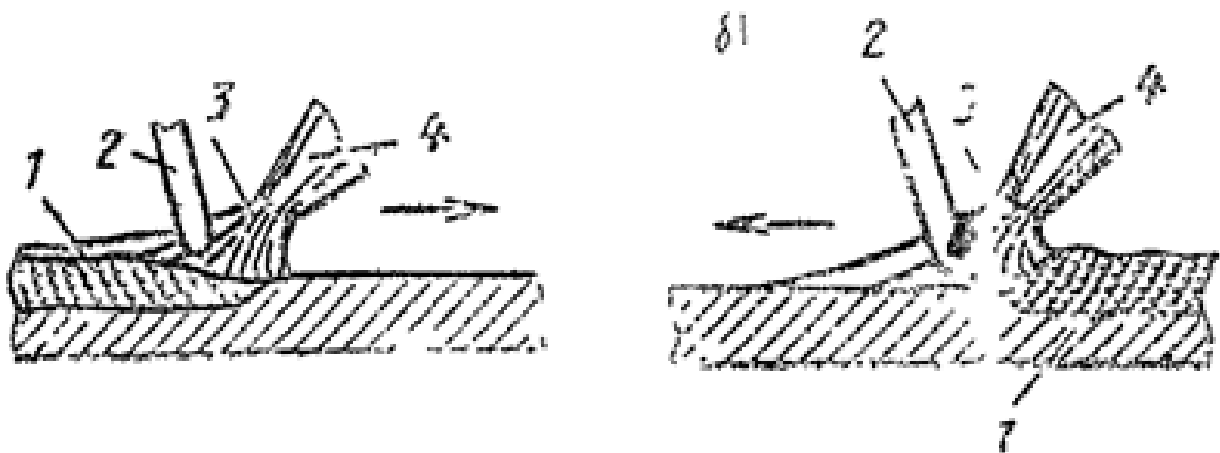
Основні способи газового зварювання: 1 – формуючий шов; 2 – присадковий пруток; 3 – полум'я горілки; 4 – горілка
